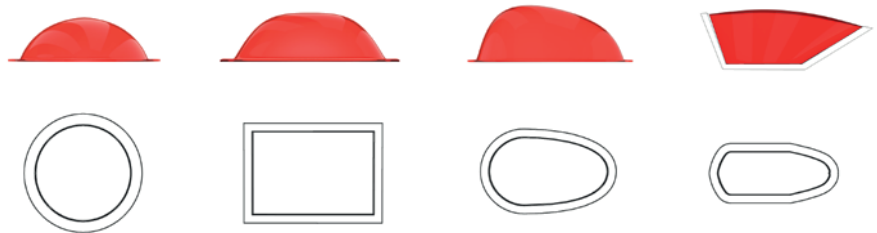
Beispiele von Grundrissformen und die daraus entstehenden Seitenkonturen
